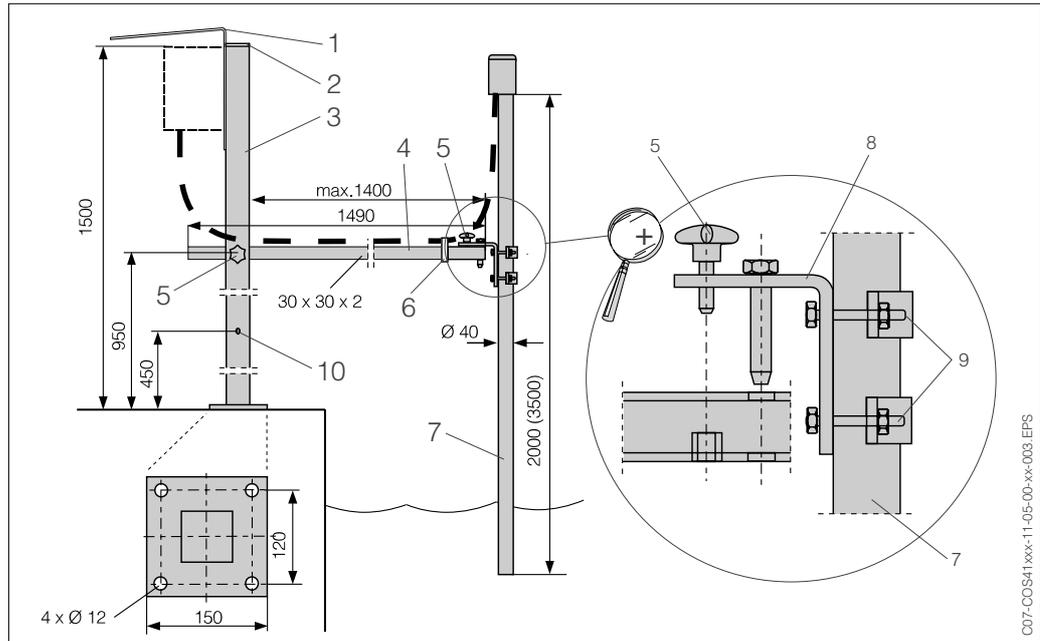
Soporte de grupo universal CYH 101-D o E
